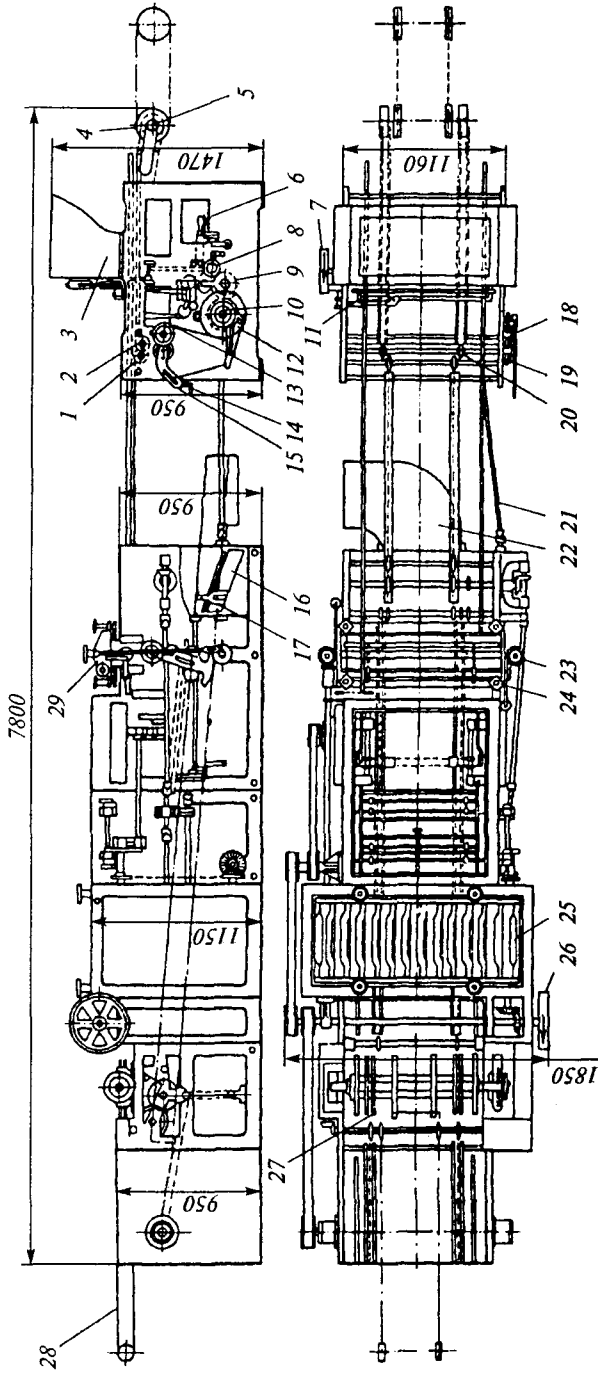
Конфетоотливочный автомат с вертикальными мерными цилиндрами
